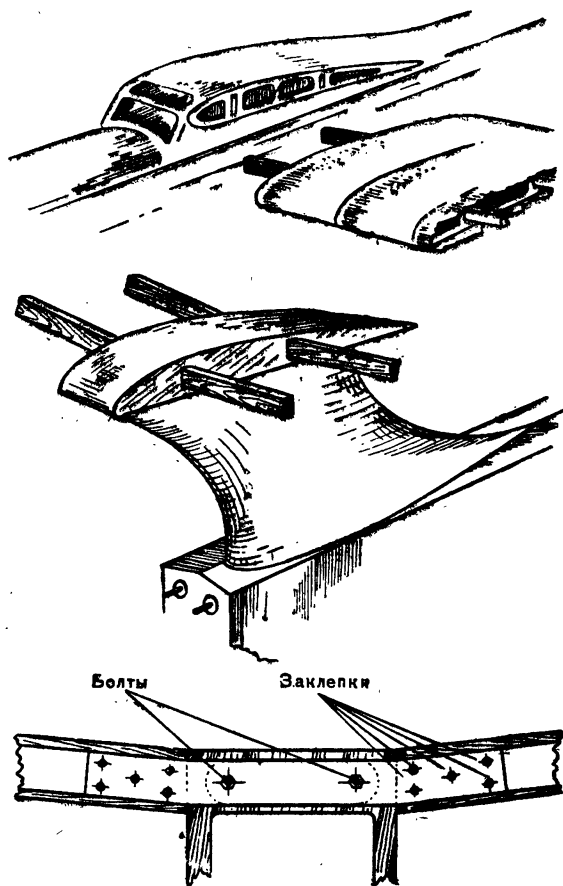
Конструкция крепления разъемного крыла с фюзеляжем.
